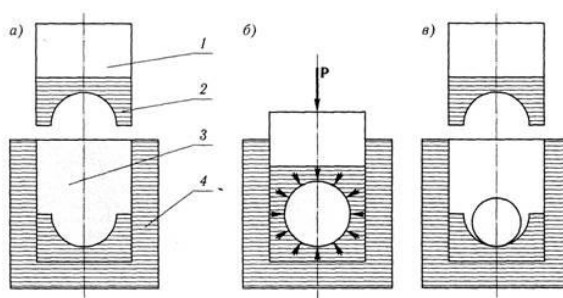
Схема квазиизостатического прессования сферической заготовки: а – загрузка пресс-формы, б – стадия прессования, в – возврат пуансона в исходное положение, 1 – металлический штамп, 2 – эластичная прессформа, 3 – пресс-порошок, 4 – матрица
